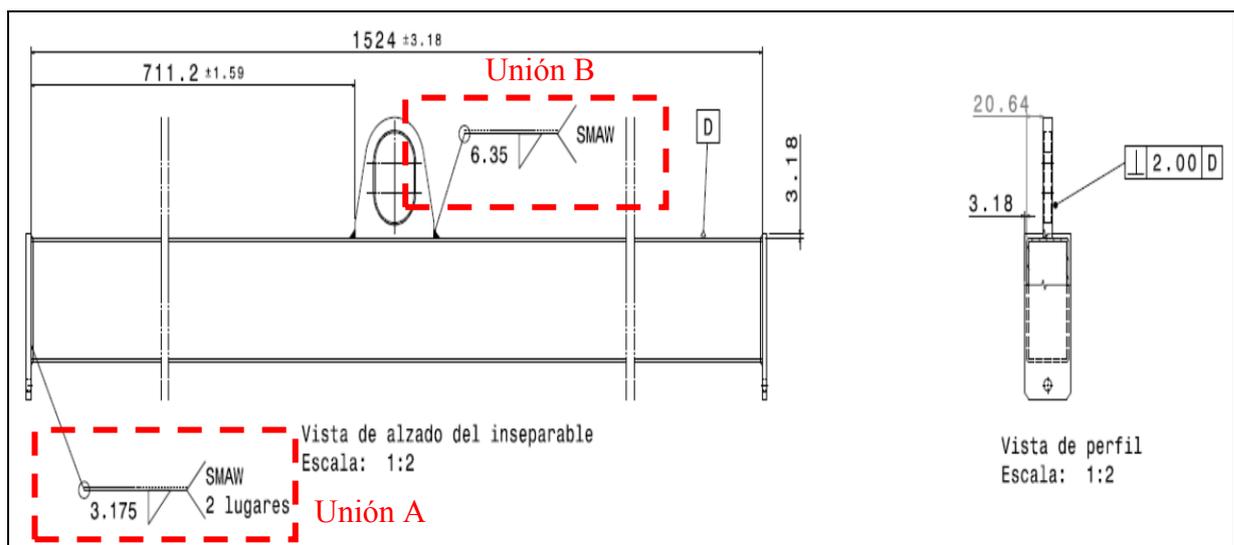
Uniones mediante soldadura en el dispositivo
